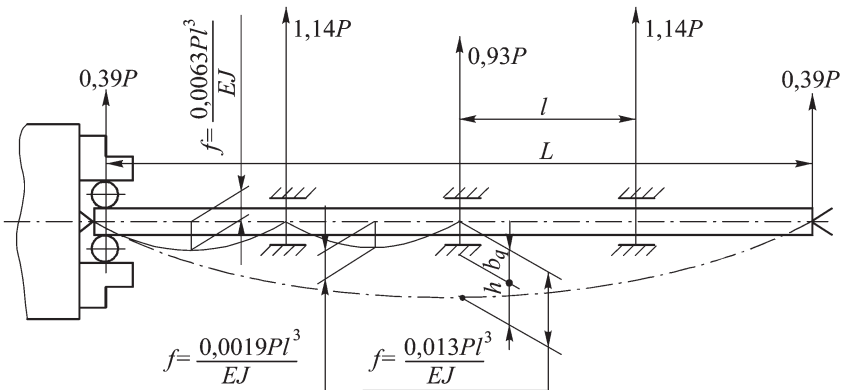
Схема установки заготовки нежесткого вала в центрах токарного станка
